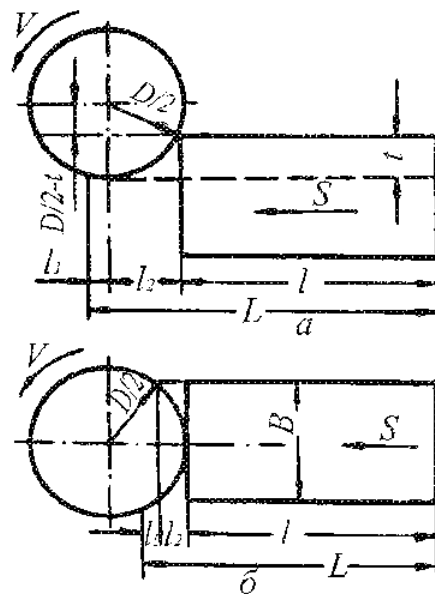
Схеми для визначення довжини врізання фрези при циліндричному (а) та торцевому (б) фрезеруванні
